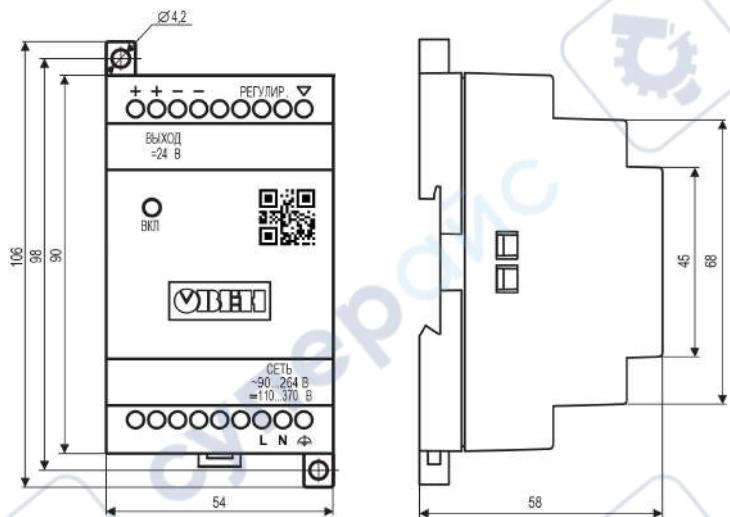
Внешний вид, габаритные и установочные размеры прибора
